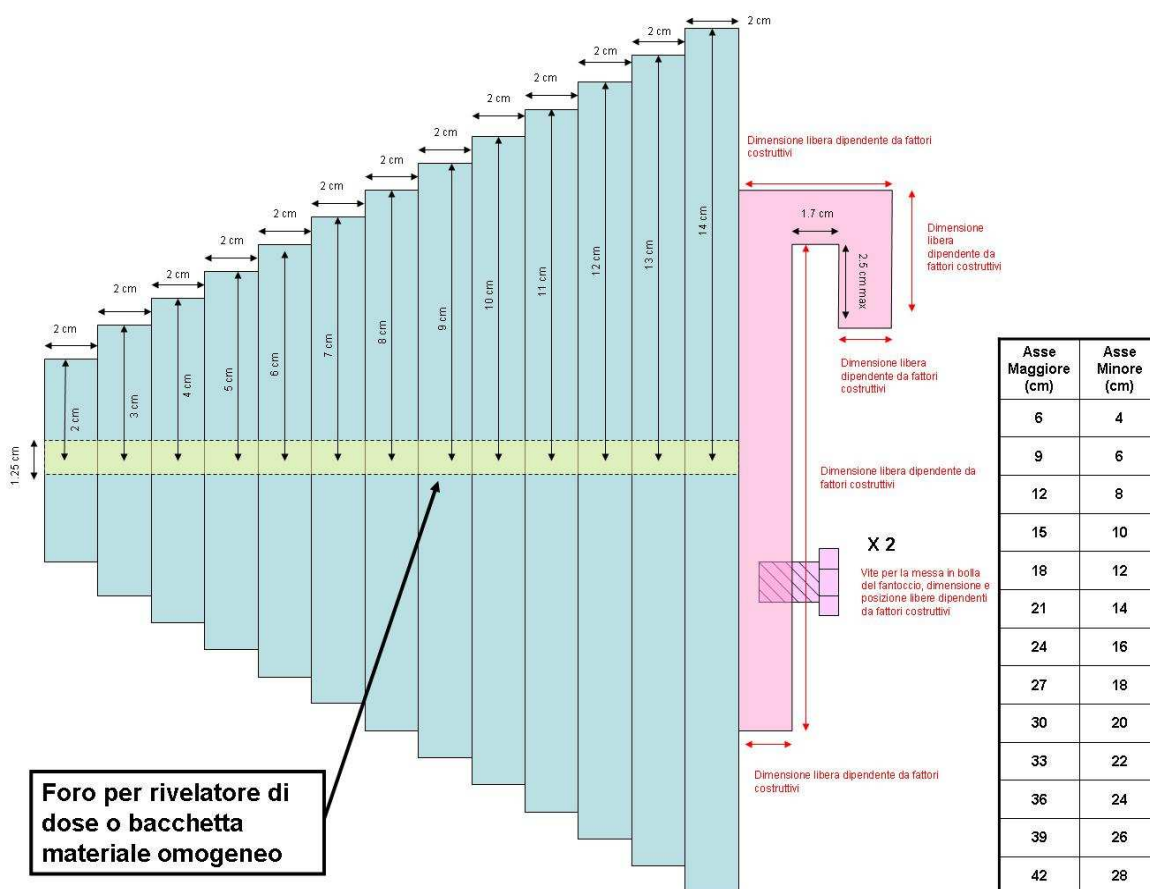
Sezione longitudinale dell'oggetto test DOSE AUTOMATICA CONO
